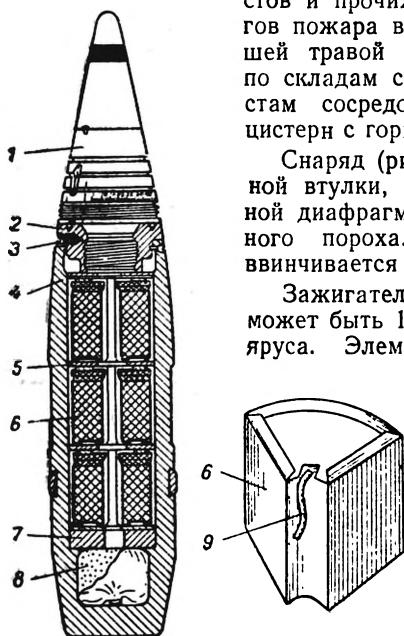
76-мм зажигательный снаряд: 1 — трубка Т-6; 2 — головная втулка; 3 — стопорный винт; 4 — корпус снаряда; 5 — прокладка; 6 — зажигательный элемент; 7 — диафрагма; 8 — вышибной заряд; 9 — стопин
